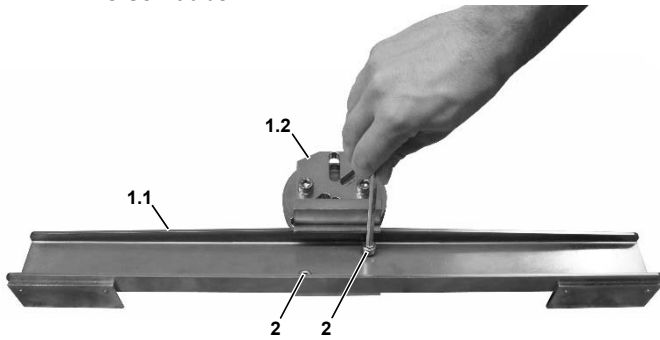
Profilschiene "1.1" mit Grundplatte "1.2" in Schraubstock einspannen.
